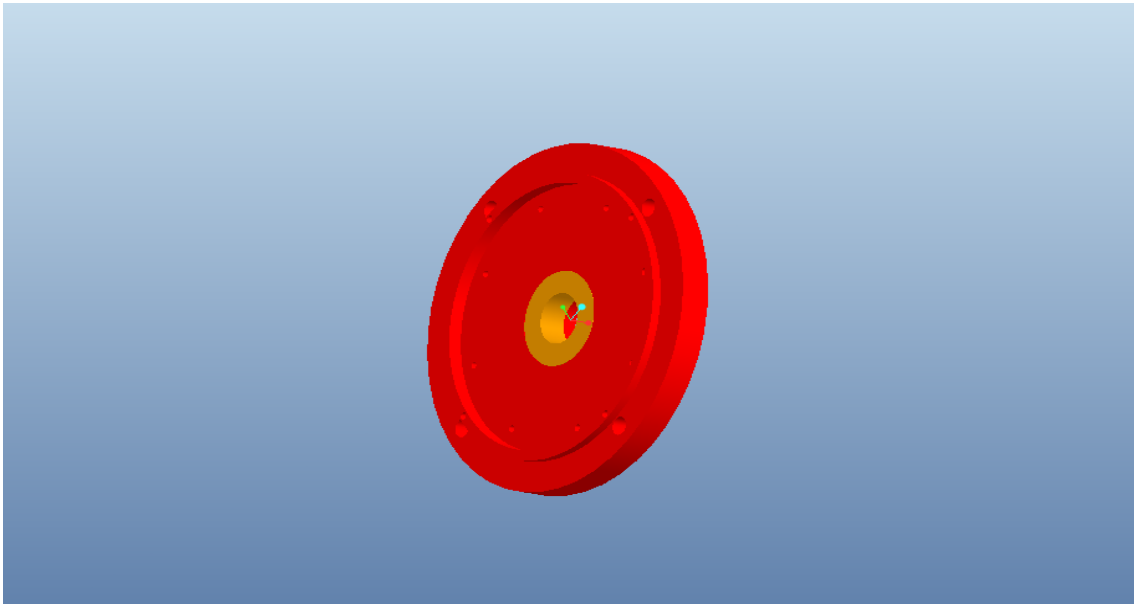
Tapa de carcasa con rodamiento trasero montado.
